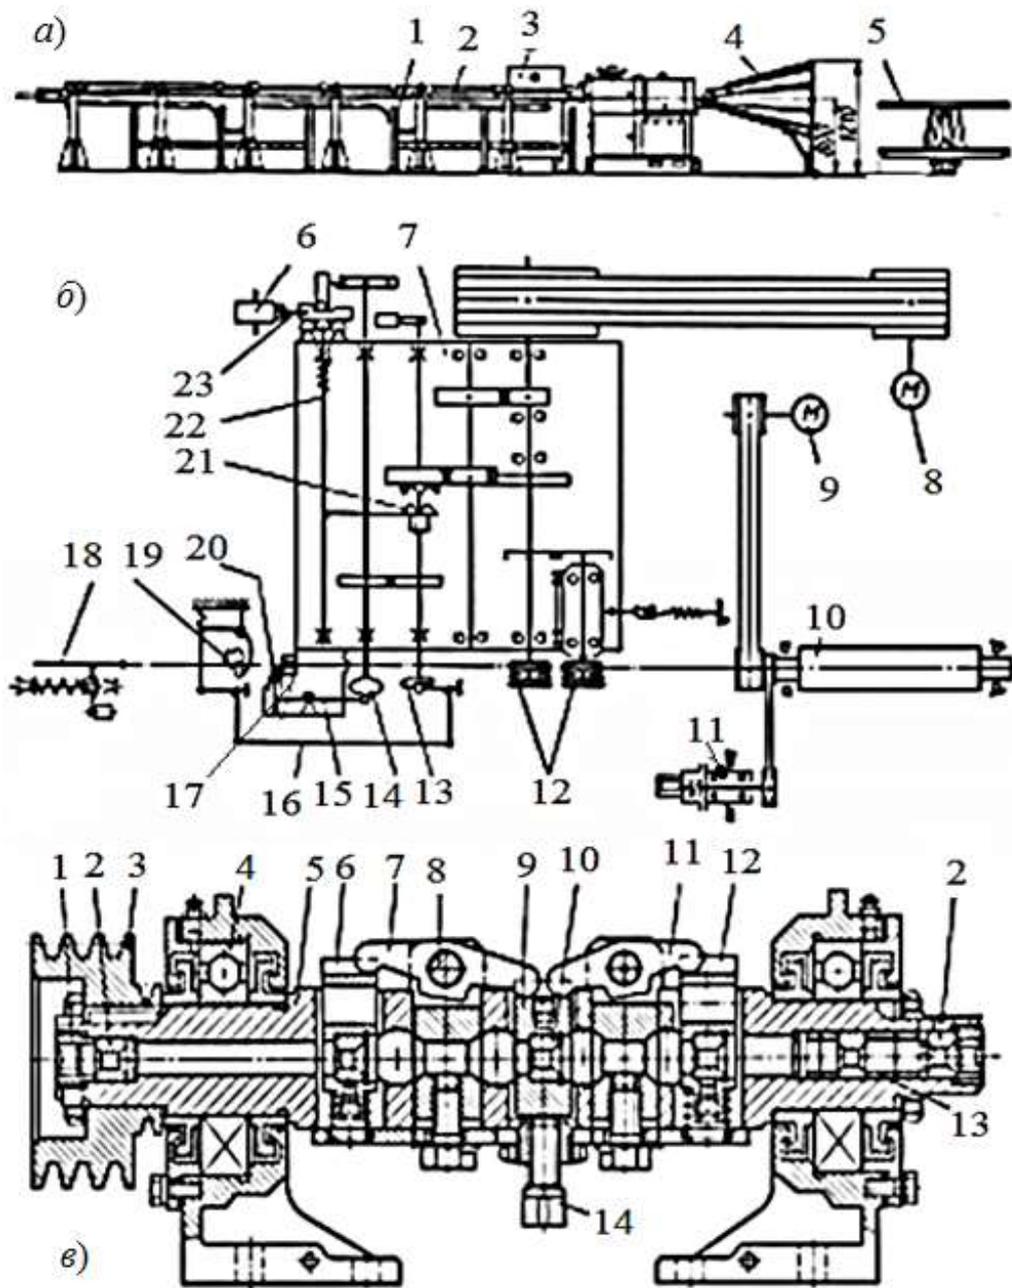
Правильно-отрезной станок СМЖ-357: а – общий вид станка; б – кинематическая схема; в – правильный барабан
